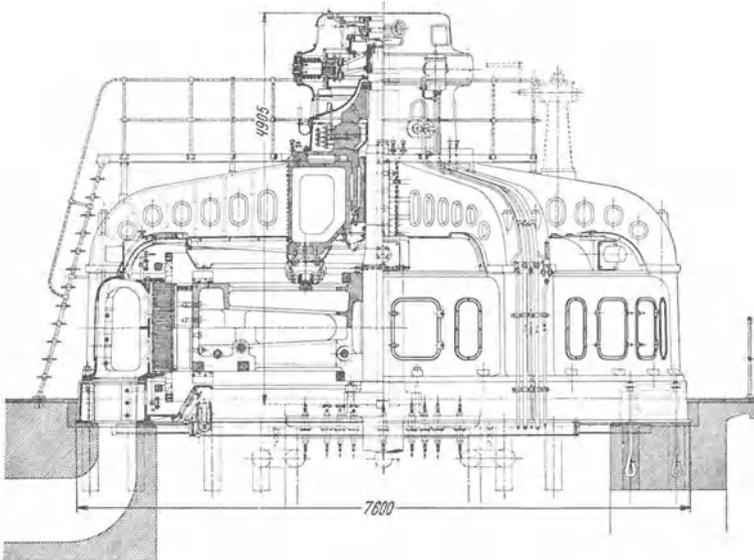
Wasserkraft-Drehstromerzeuger auf Gußsockel für hohe Drehzahl; hohe Maschine — kleiner Durchmesser. 8 MVA, 17,6 kV,  $n = 166,6$  U/min.
